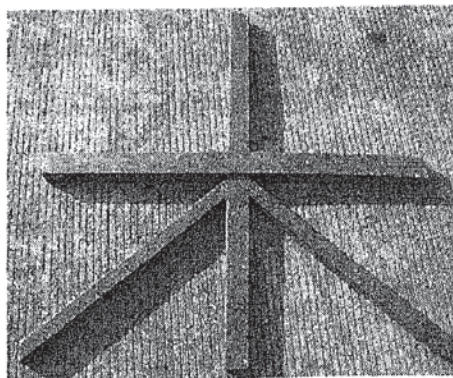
Элемент корпуса автобуса – балка продольного пояса с приваренными к ней оконной стойкой и деталями боковины
